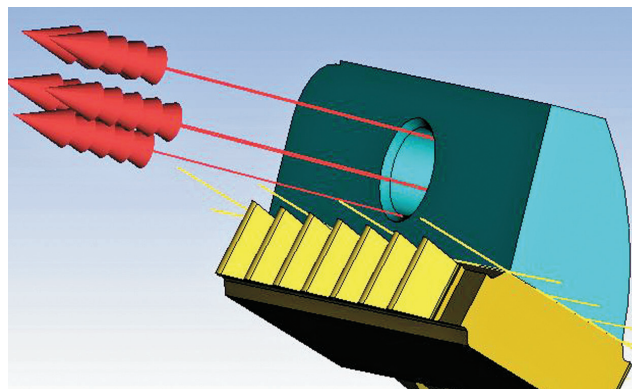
Крепление твердосплавной пластины в корпусе фрезы
